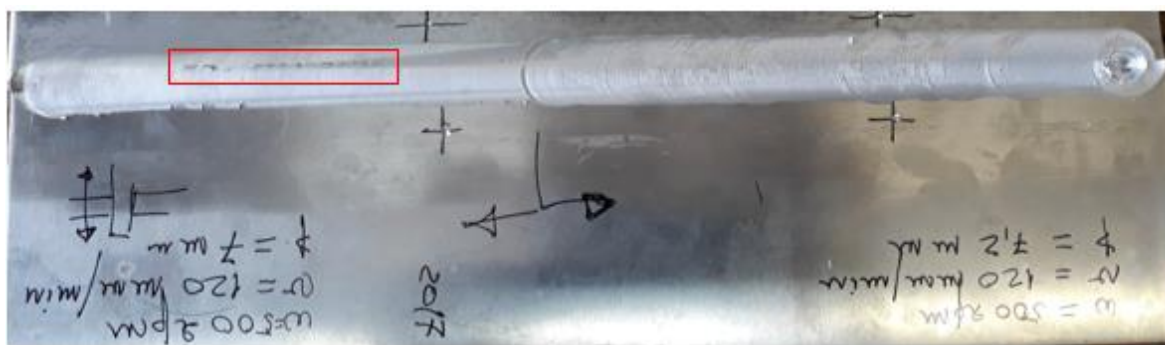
Estado superficial das soldaduras 562BRP-3 (à esquerda) e da série 562BRP-4 (à direita)
